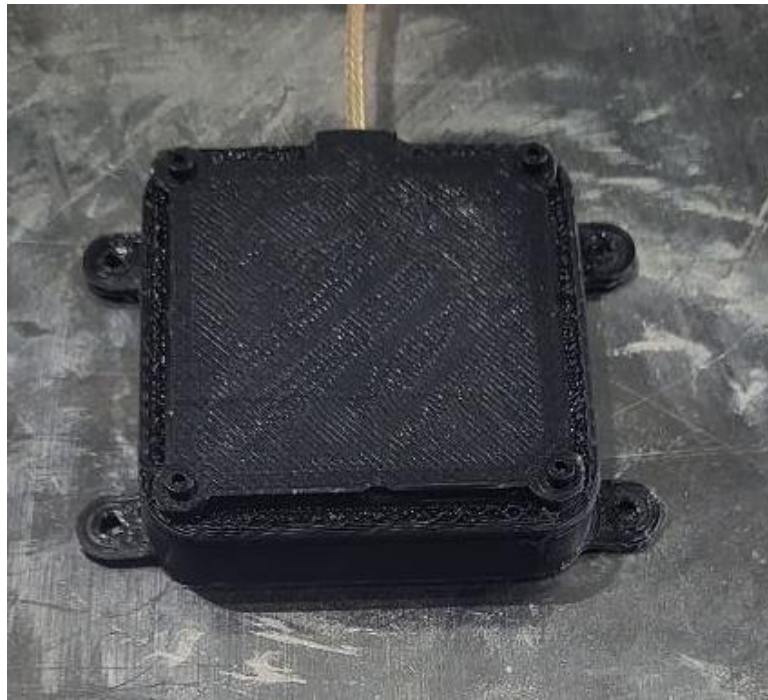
Корпус датчика БПЛА, из материала PETG
